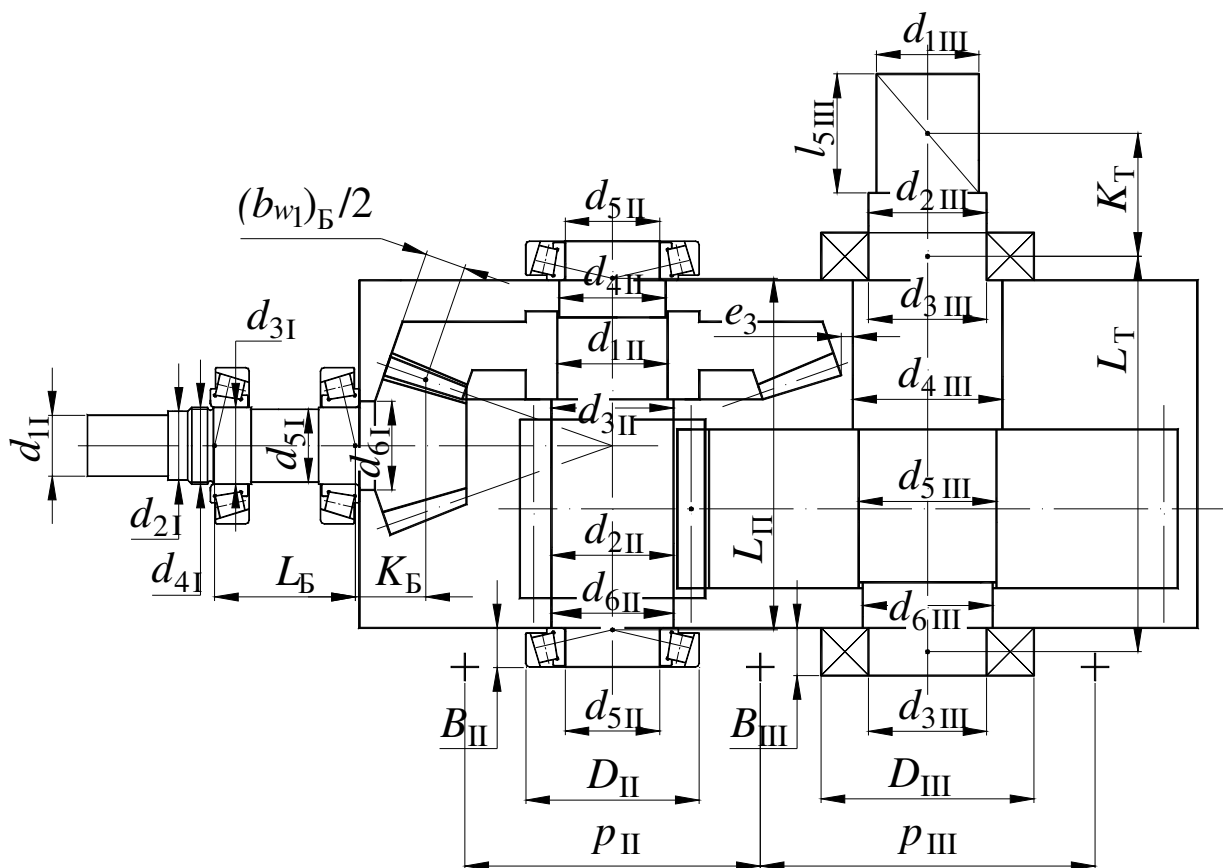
Окончательный результат эскизной компоновки редуктора
